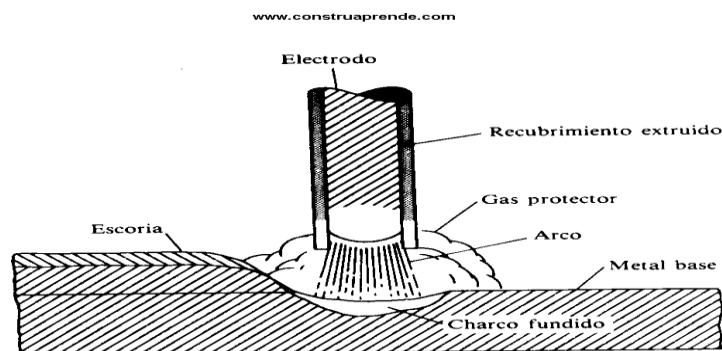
Elementos del proceso de soldadura de arco metálico protegido (SMAW). Fuente: *Guide to Shielded Metal Arc Welding SMAW (2022)*.
